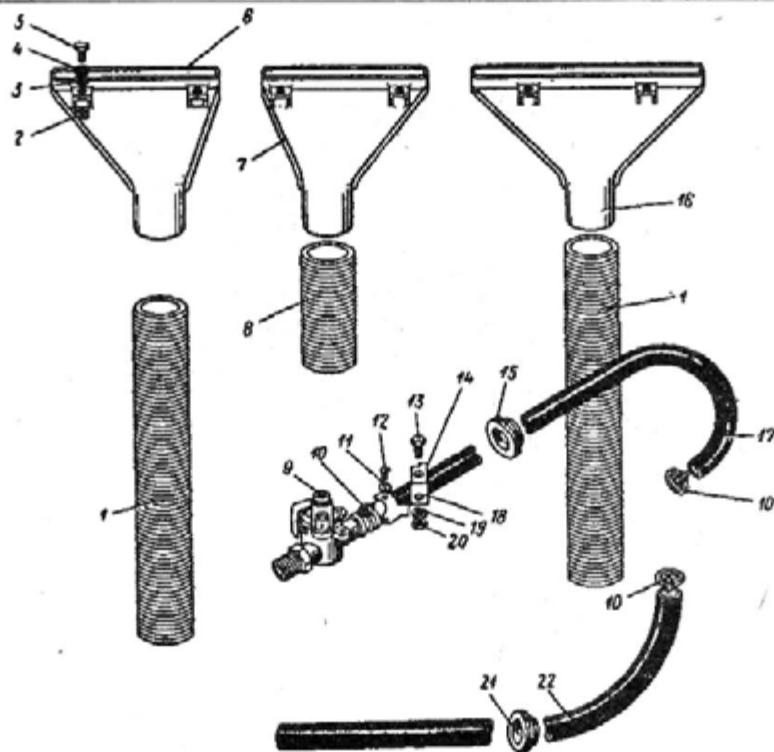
Детали отопителя кузова и обогревателя ветрового стекла
